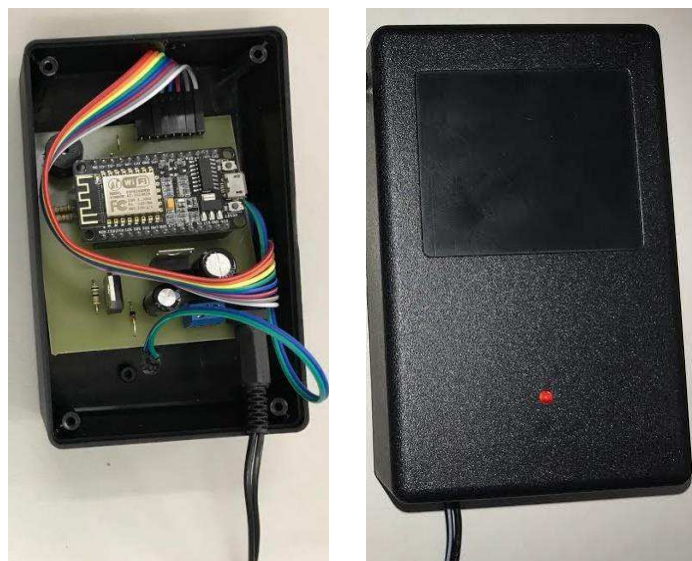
Componentes soldados na placa de circuito montado.
